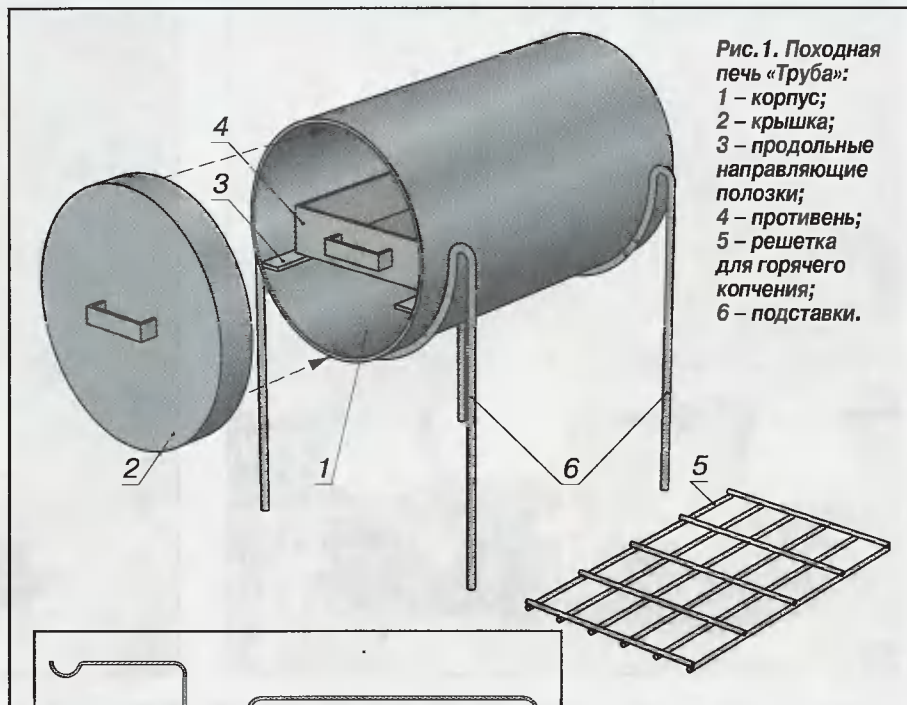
Походная печь «Труба»: 1 — корпус; 2 — крышка; 3 — продольные направляющие полозки; 4 — противень; 5 — решетка для горячего копчения; 6 — подставки.
